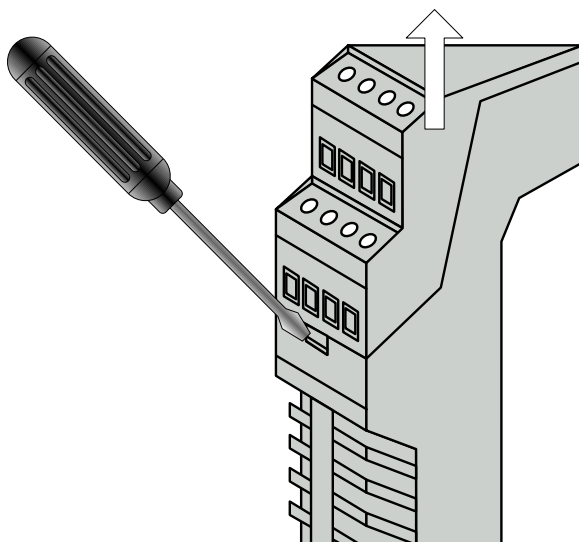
Извлечение платы блока BIC-4 из корпуса
